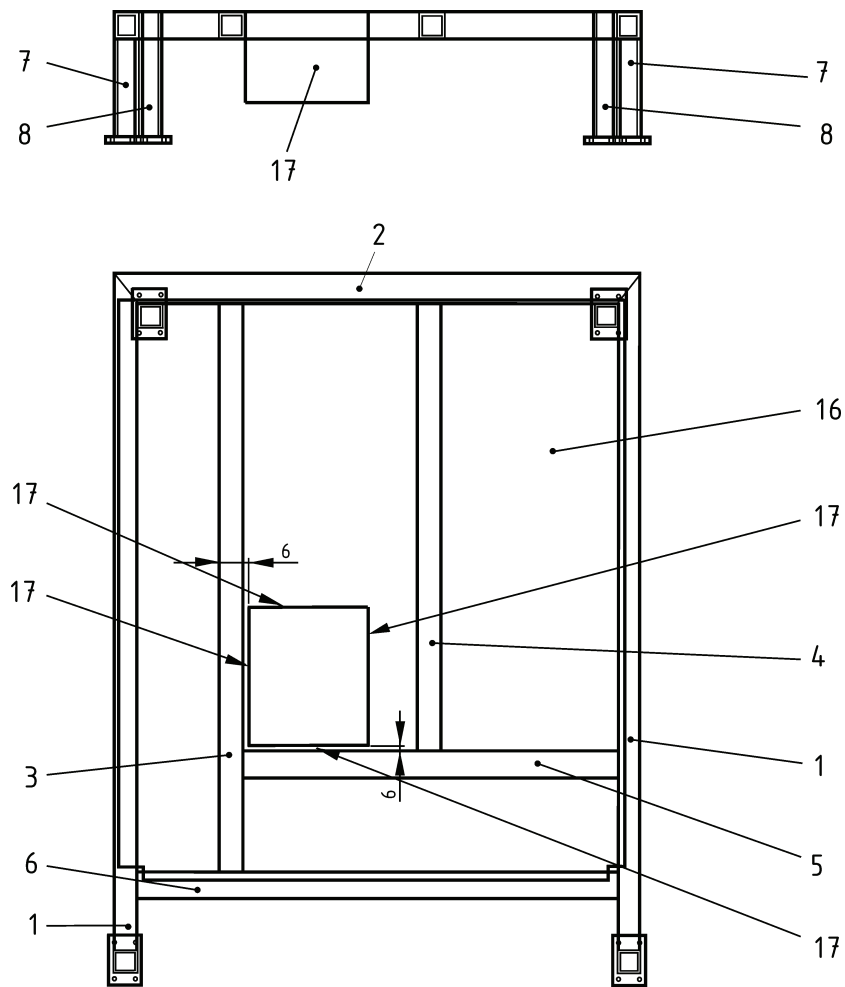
Probenträgerwagen, geschweißte Teile, Ansichten und Schnitt A
